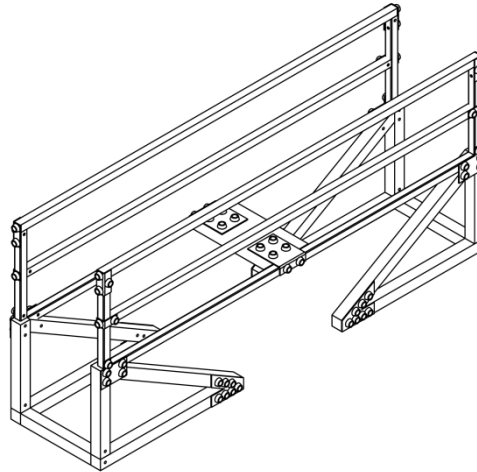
6: Vista isométrica del ensamblaje del soporte 3. Fuente: Elaboración propia.
